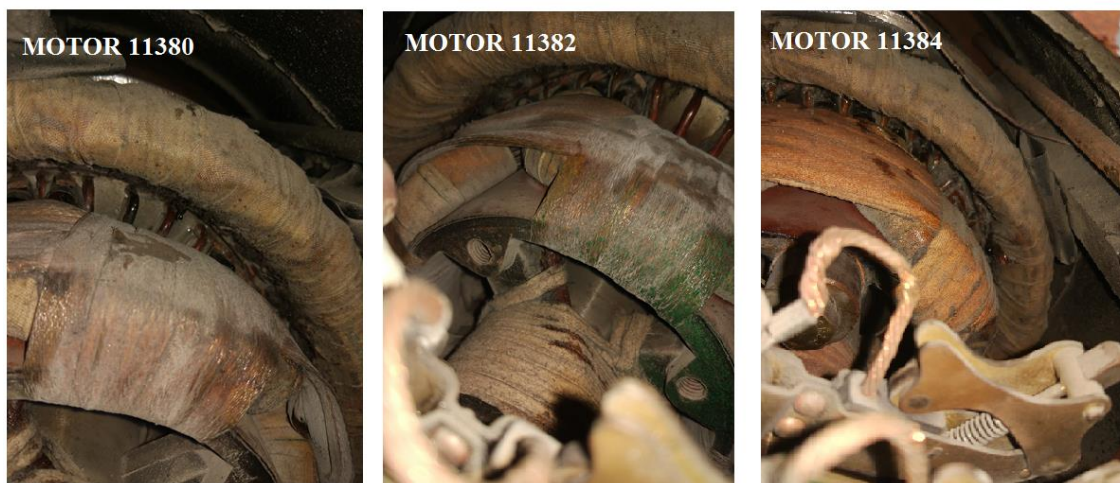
Inspección del estado interno interna del motor 11380,11382,11384
